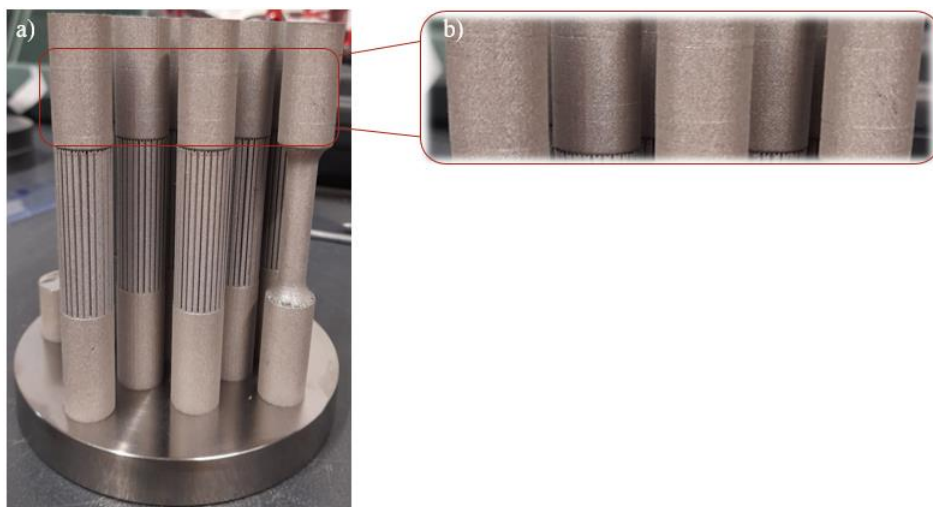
a) Provetes do terceiro lote, b) pormenor com a presença de fissuras.
